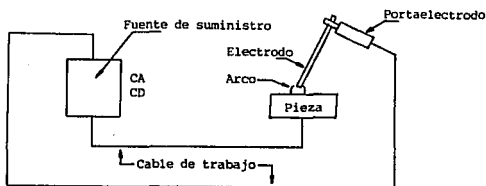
Circuito de soldadura por arco eléctrico.
